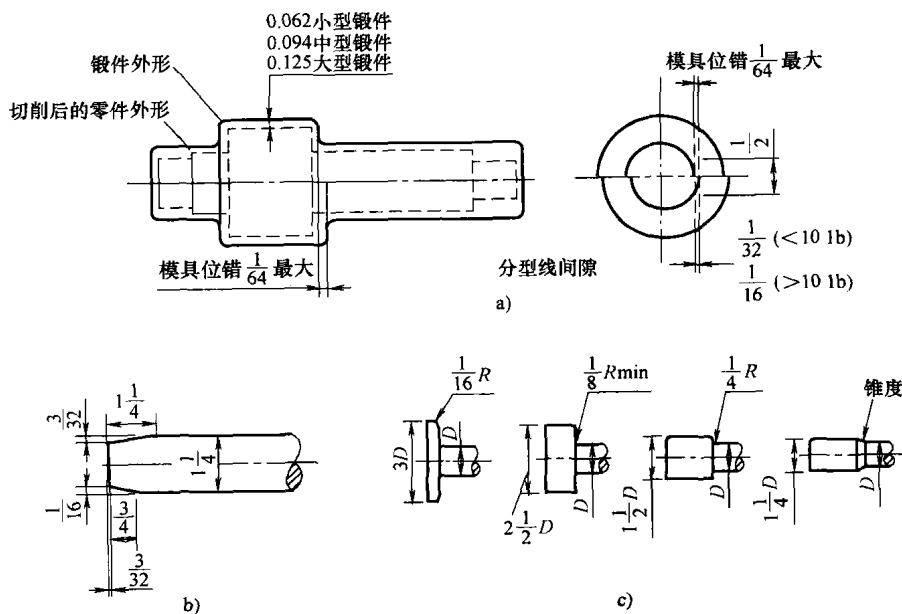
热轧锻件的切削加工裕量。图示这些零件都是锻粗零件中最为简单的形状。图中尺寸为 in
